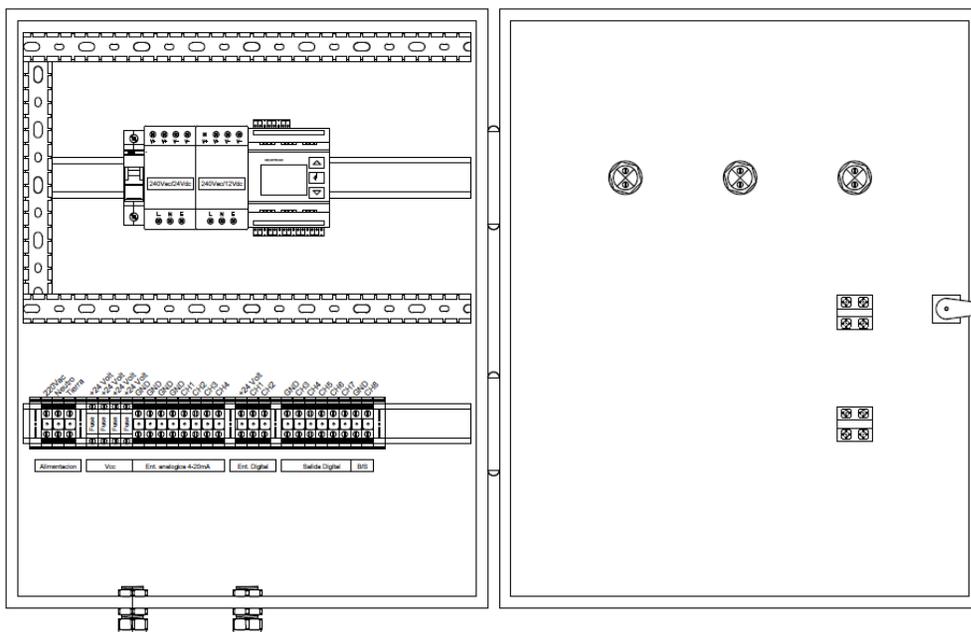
Disposición de elementos dentro del tablero (interior)
